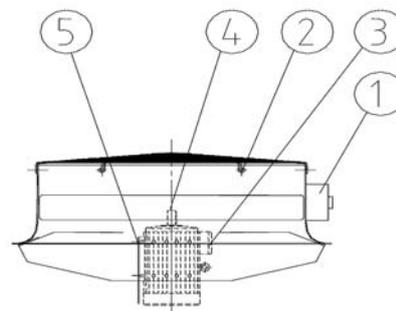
Вентилятор в сборе: 1: защитный выключатель, 2: защитная решётка вентилятора, 3: соединительная коробка, 4: стопорный винт вентилятора и 5: винт крепления двигателя
